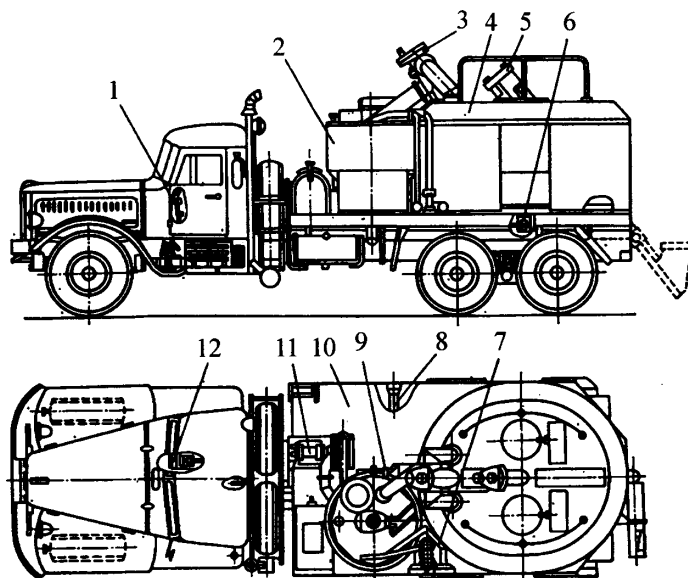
Агрегат 4ПА: 1 – пульт управления; 2 – аккумулятор; 3 – рабочий шнек; 4 – сварной бункер; 5 – загрузочный шнек; 6 – пневмовибратор; 7, 8 – соответственно приемный и раздаточный коллекторы; 9 – регулятор выдачи сыпучего материала; 10 – рама автошасси КрАЗ – 257; 11 – центробежный песковой насос 5ПС-10; 12 – гидросистема
